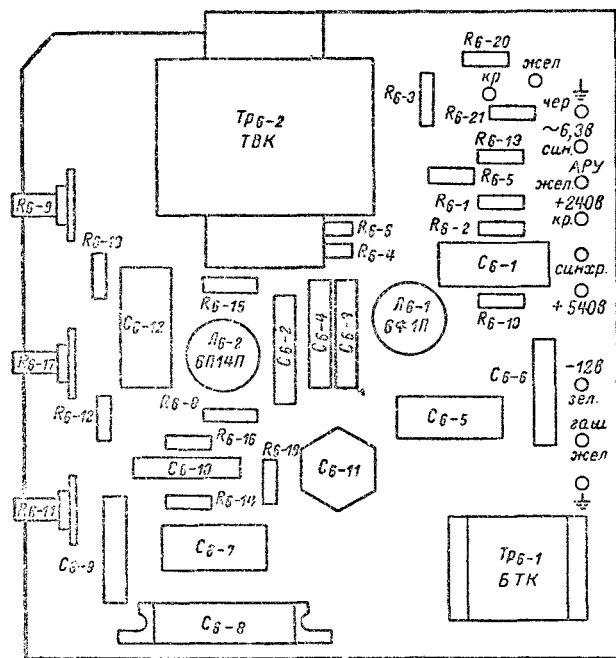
Расположение деталей на плате кадровой развертки телевизора «Нева».
